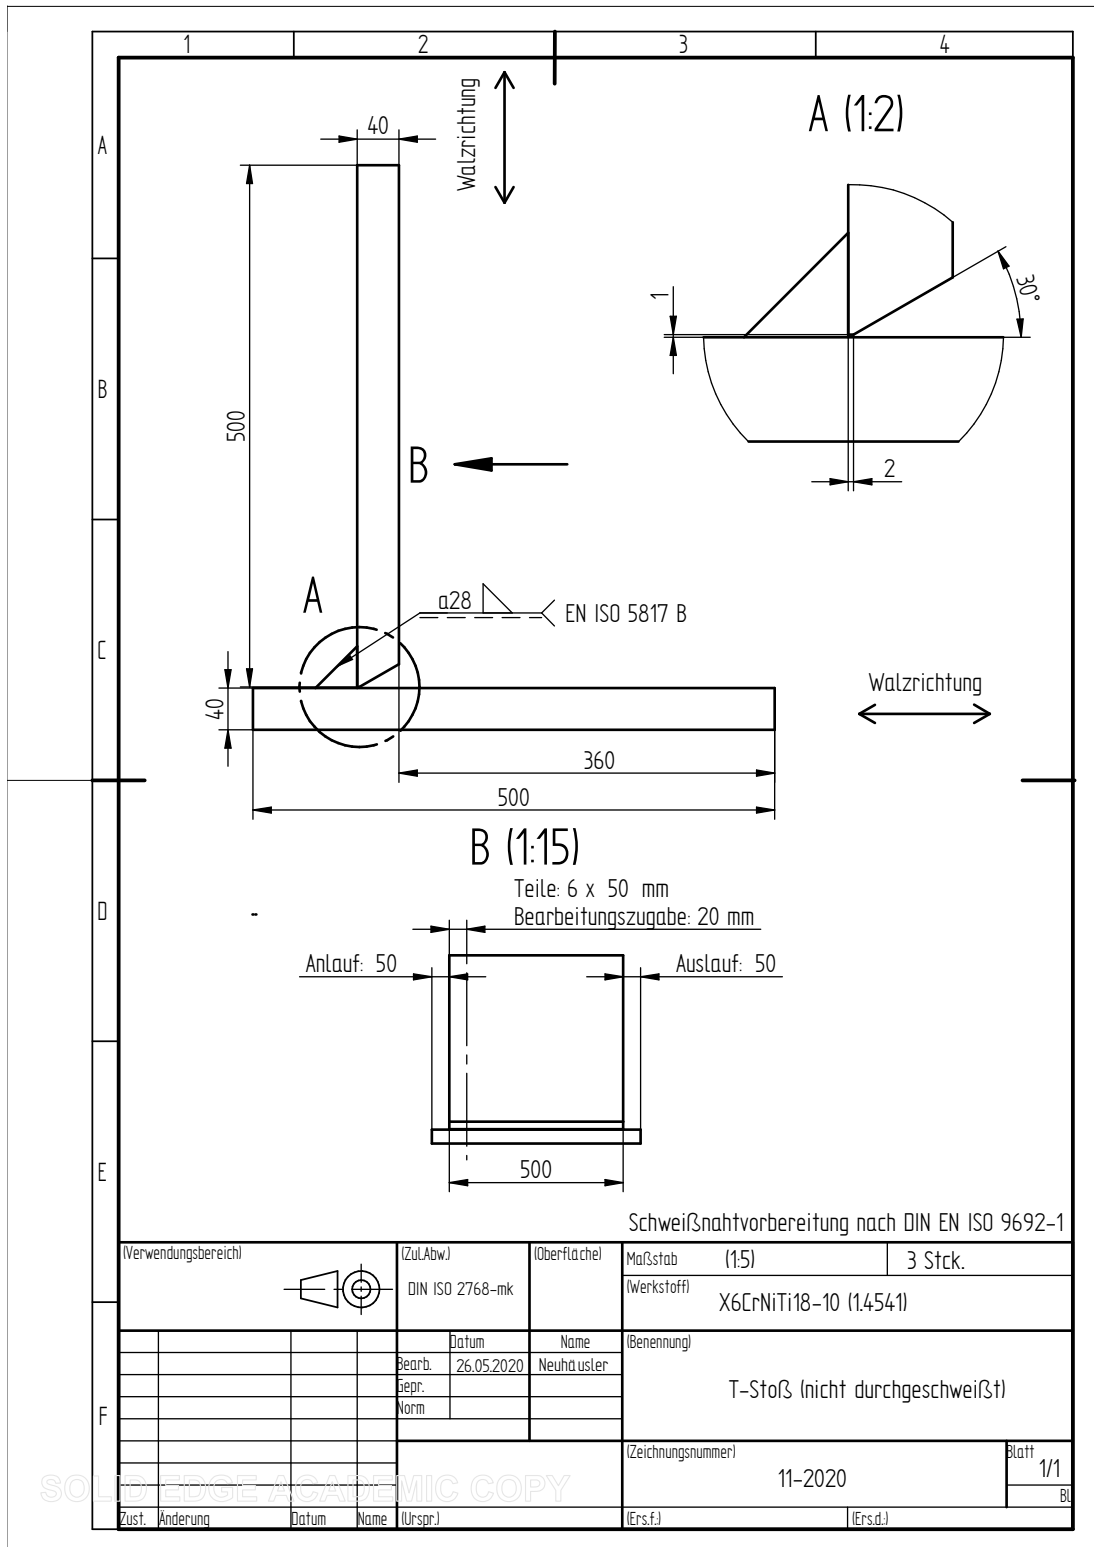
Fertigungszeichnung für die T-Stoß Proben aus 1.4541 [67].
